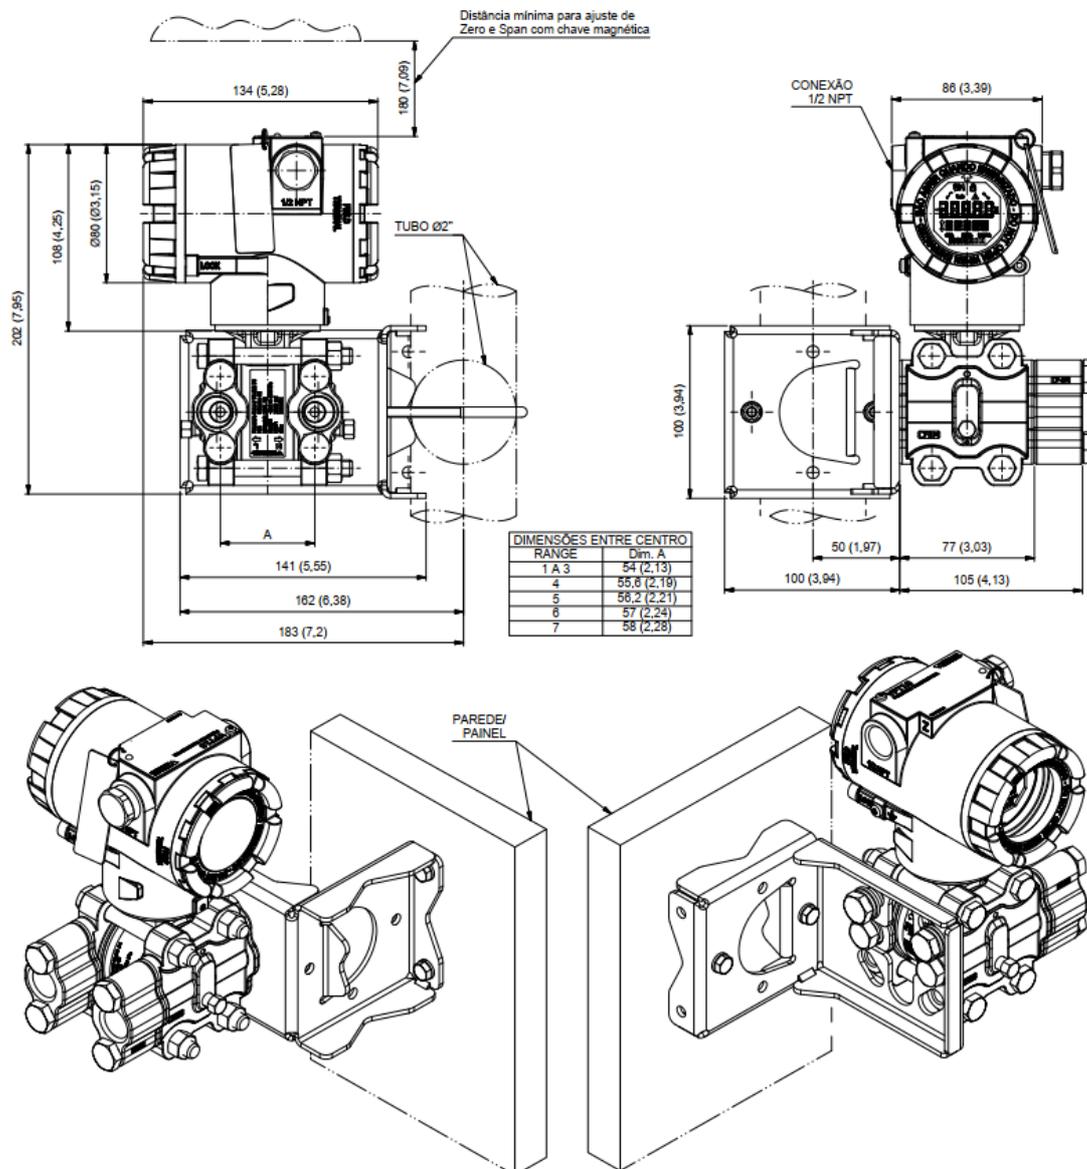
Desenho dimensional e esquema de montagem do VPT10 HART padrão.
